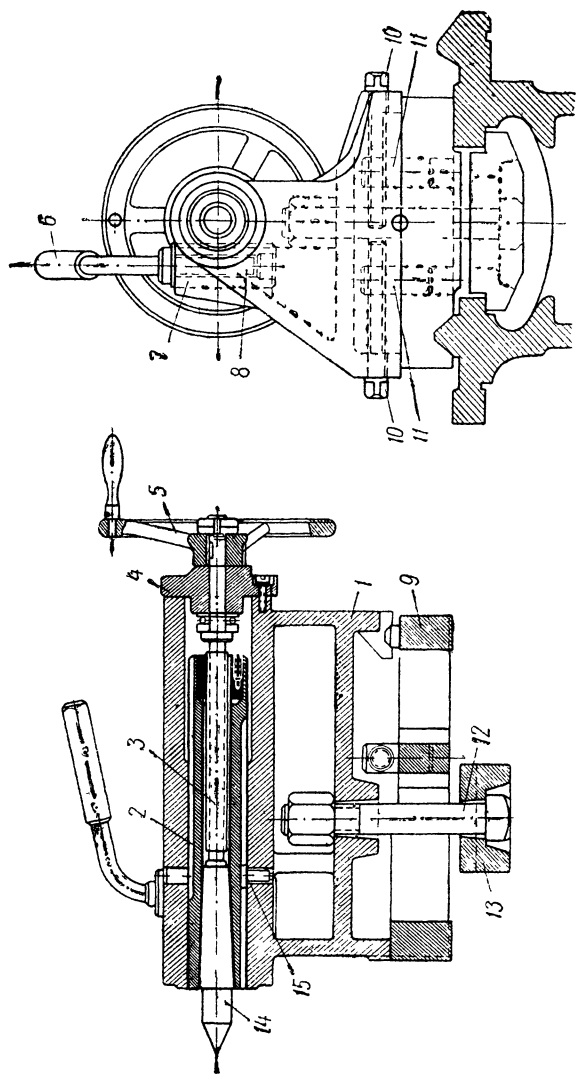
Задняя бабка токарно-винторезного станка модели 1615-М.
